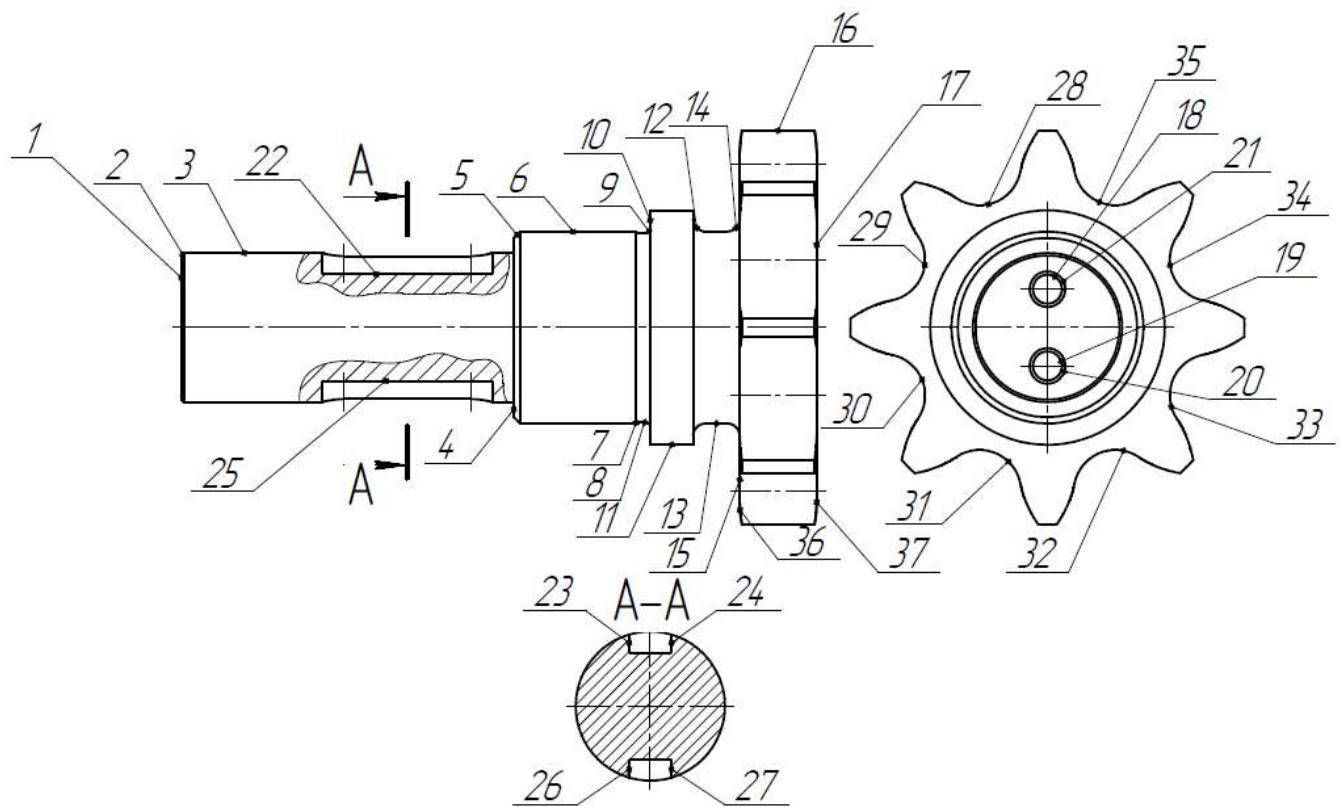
Ескіз деталі з нумерацією поверхонь
